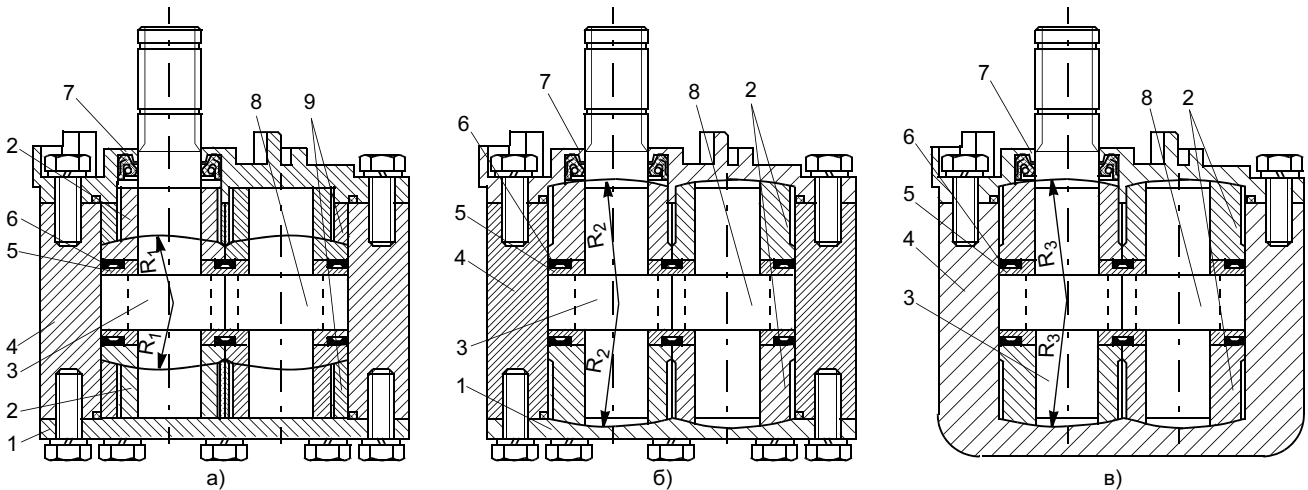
Шестеренные насосы различной компоновки с самоустанавливающимися подшипниками
